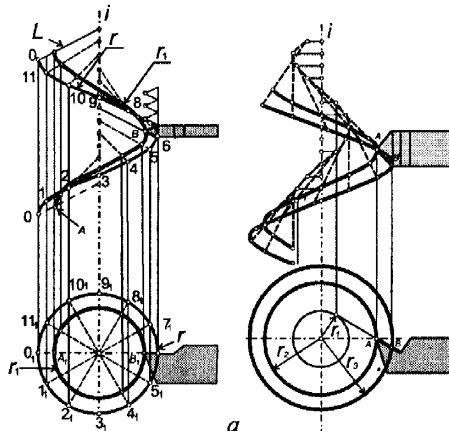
Схема виготовлення токарним різцем гвинтових поверхонь
